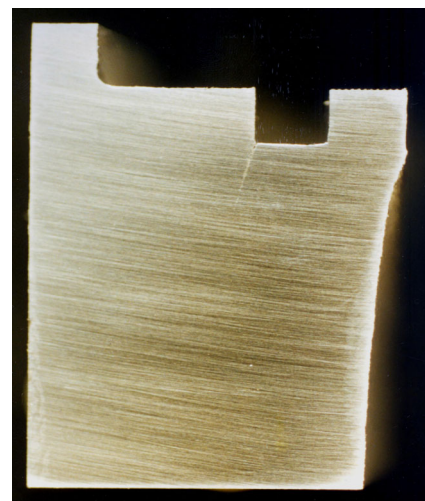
Componente de grúa roto por fatiga. La fractura (a la derecha de la figura) fue promovida por un mal diseño, que dio lugar a la aparición de grietas en zonas de concentración de tensiones. Una grieta similar a la que originó la rotura puede observarse en la figura.
